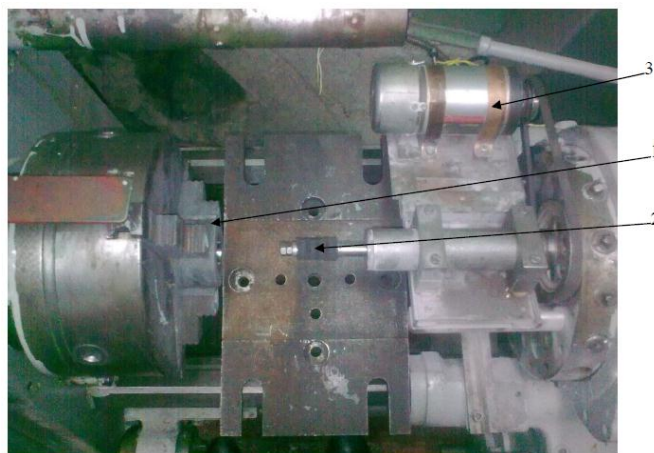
Вид зверху на експериментальну установку для МАО внутрішніх поверхонь на базі токарно-револьверного верстата: 1 - заготовка з ВК6 в патроні верстата; 2 - оправлення з магнітними кільцями; 3 - привід обертання оправлення
